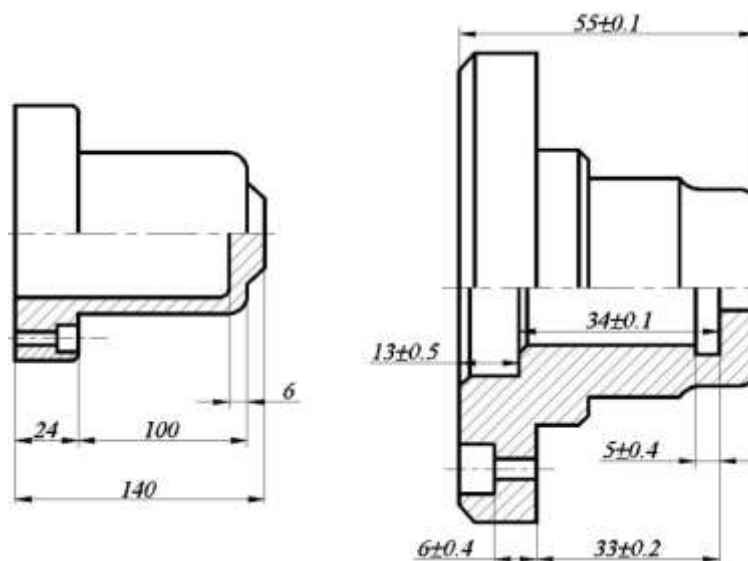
Пример простановки размеров на рабочих чертежах деталей
